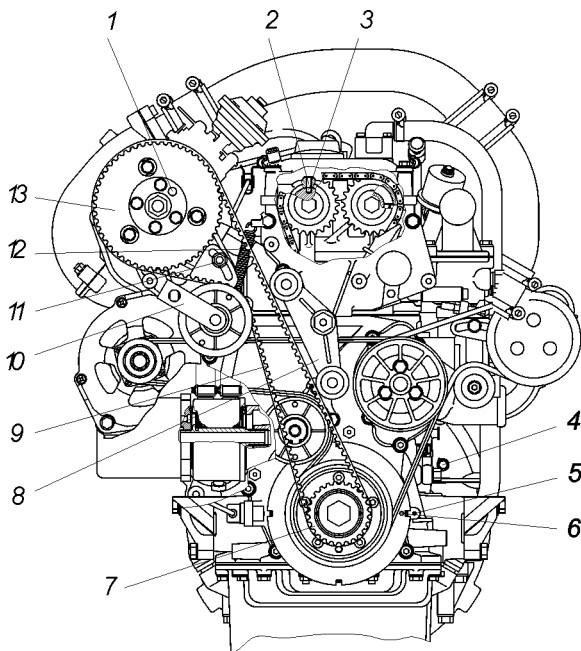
Расположение меток и отверстий под штифты для замены ремня привода ТНВД:
